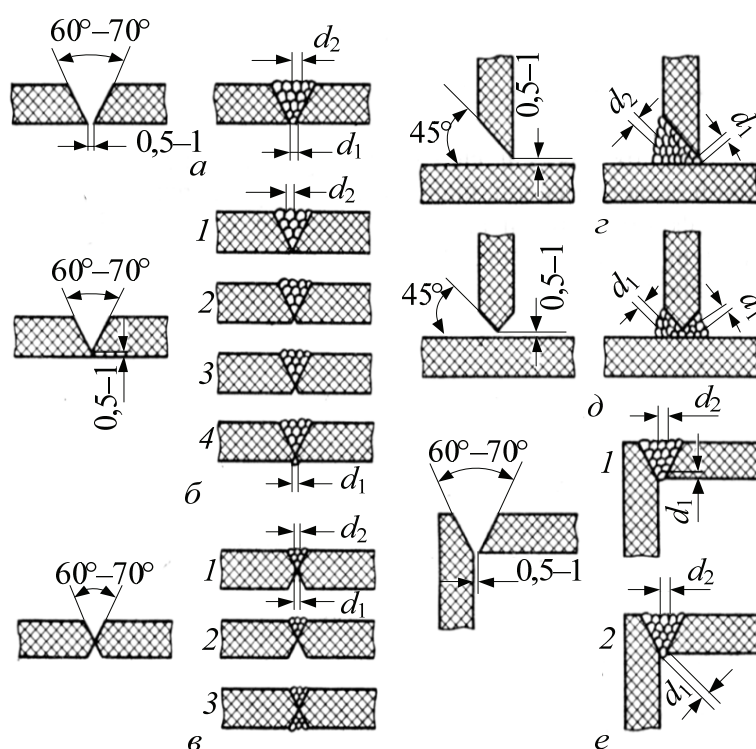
Основные типы сварных швов при сварке горячим газом с присадочным прутком:
